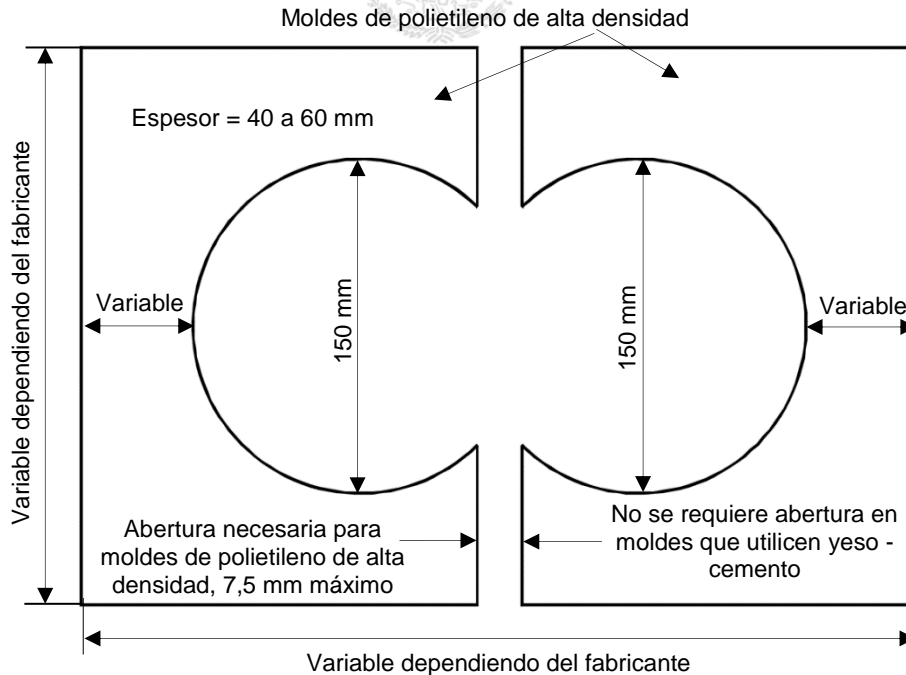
Molde para espécimen cilíndrico de 150 mm de diámetro
